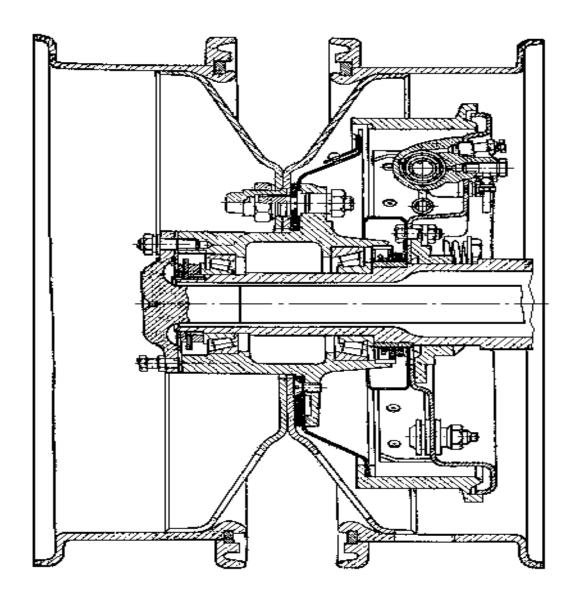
Ступица и два обода ведущего колеса грузовика
